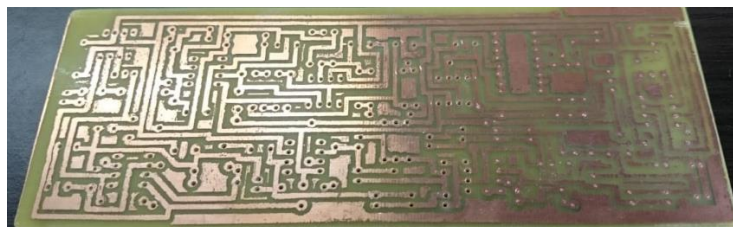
Circuito Impreso PCB acondicionador pequeña señal
